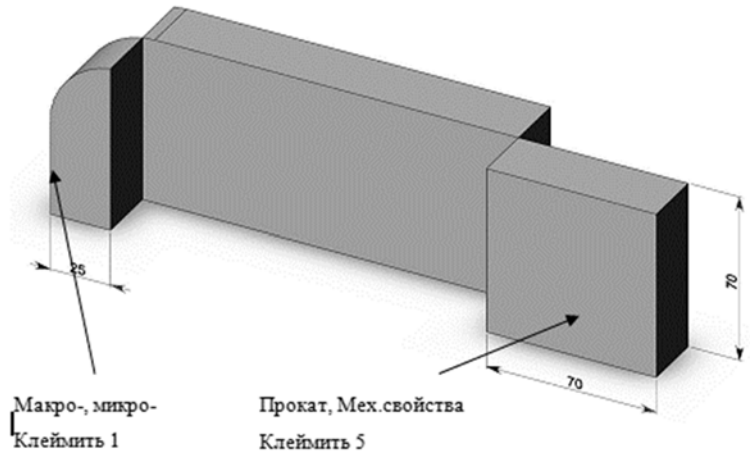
Схема раскроя на образцы заготовки №1
